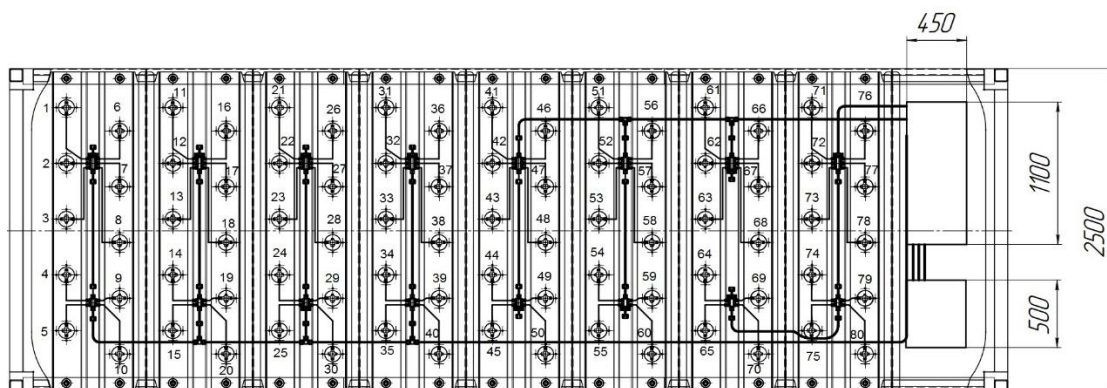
Схема размещения оборудования ПАГЗ-5000-24,5-3-CH₄
